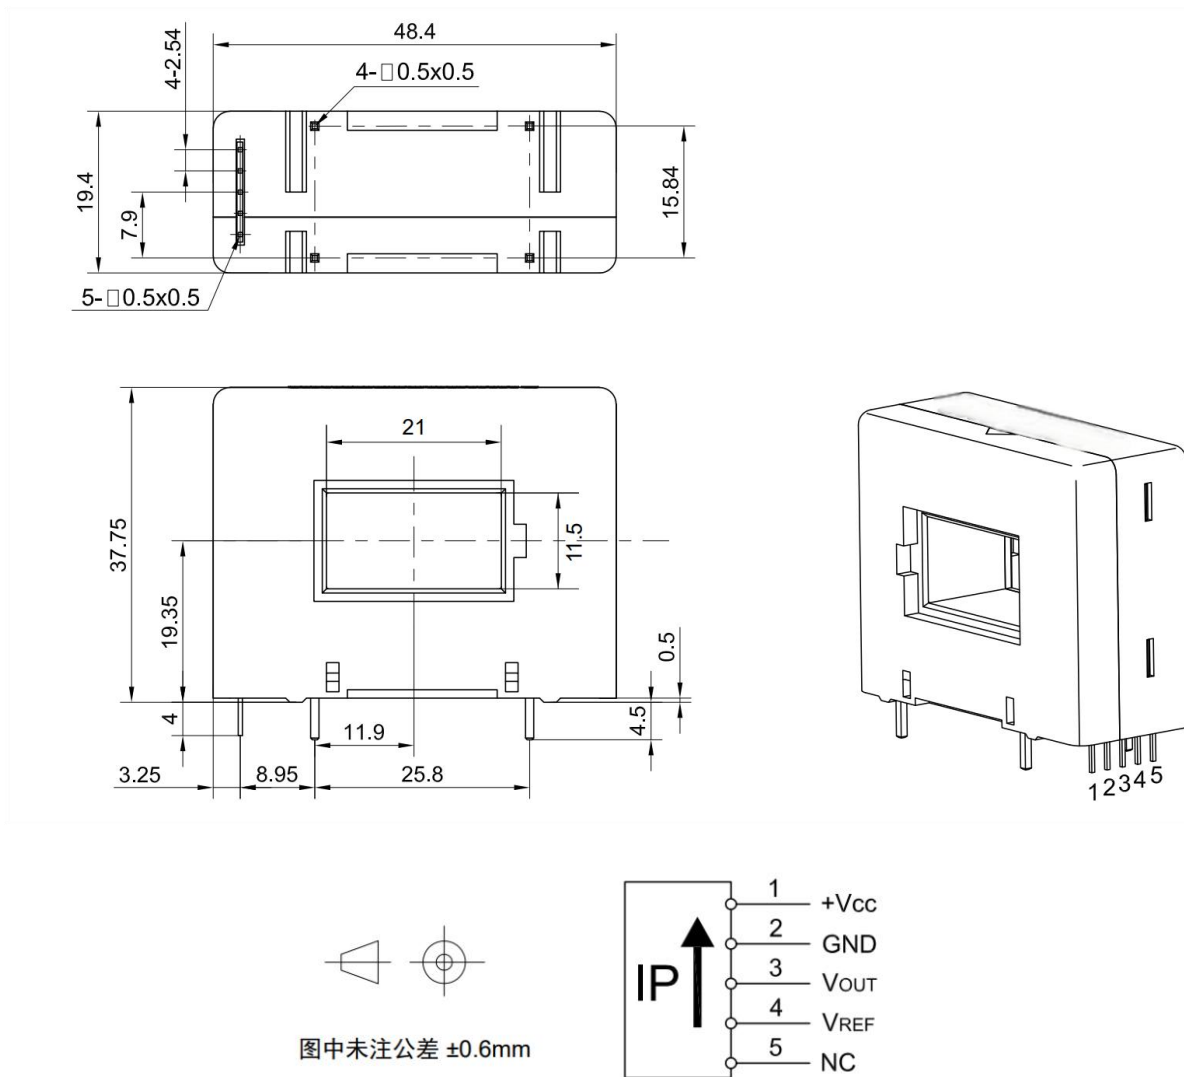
外形尺寸图（尺寸单位：mm）/Figure 12 Overall dimensions (size unit: mm)
